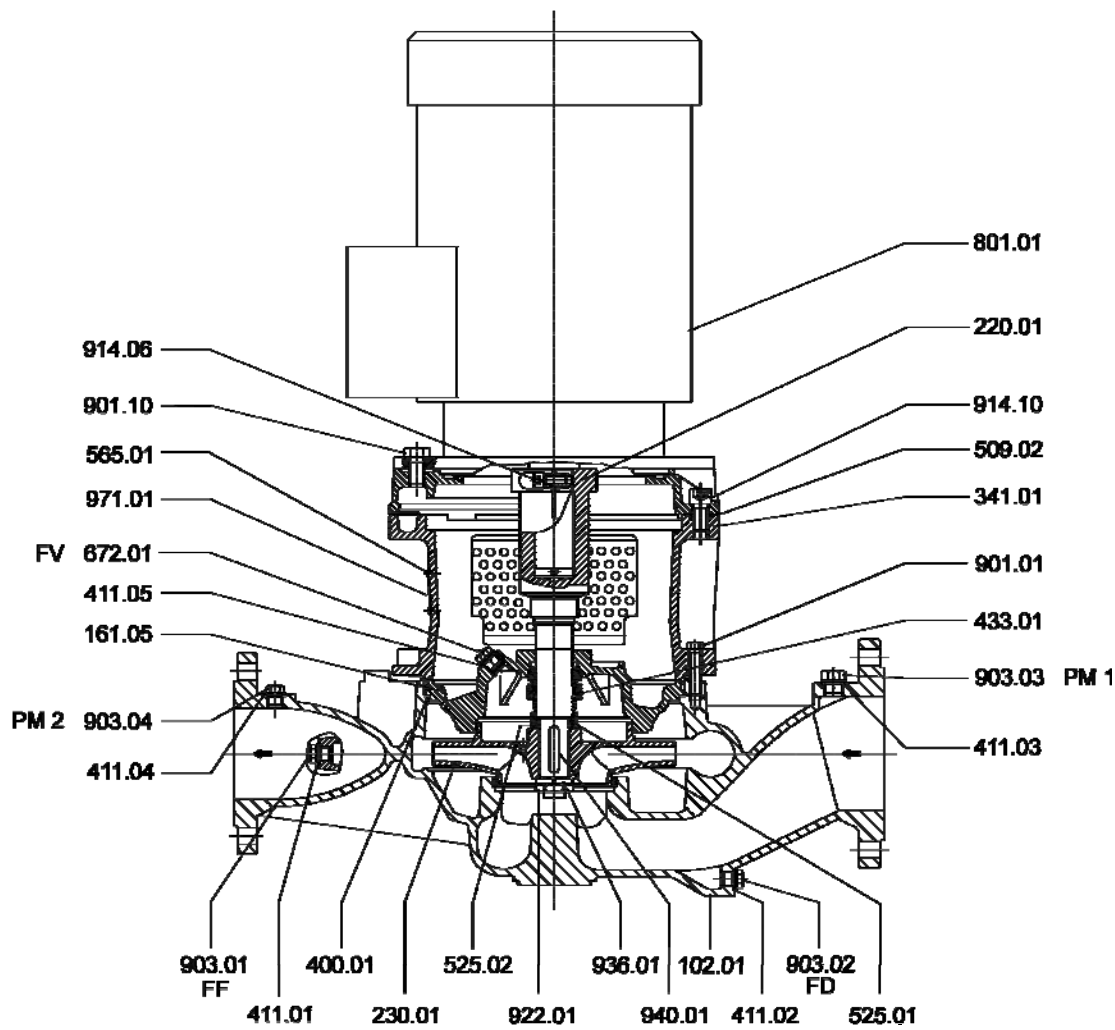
U3...D – Торцевое уплотнение под нагрузкой – типоразмеры с диаметром 40 на уплотнении вала
